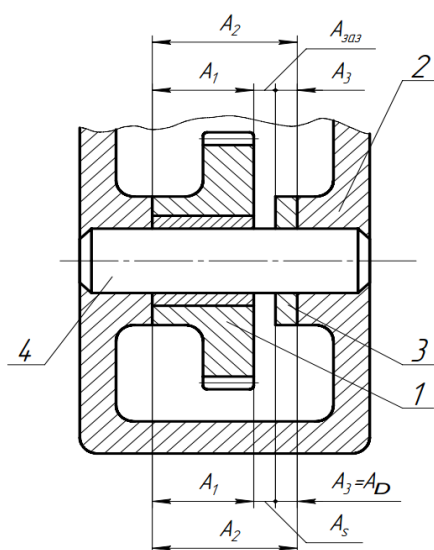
Фрагмент сборочного чертежа редуктора с размерной цепью
